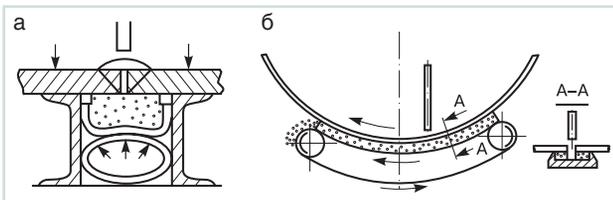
Флюсовая подушка для сварки прямолинейных (а) и кольцевых (б) стыковых соединений
